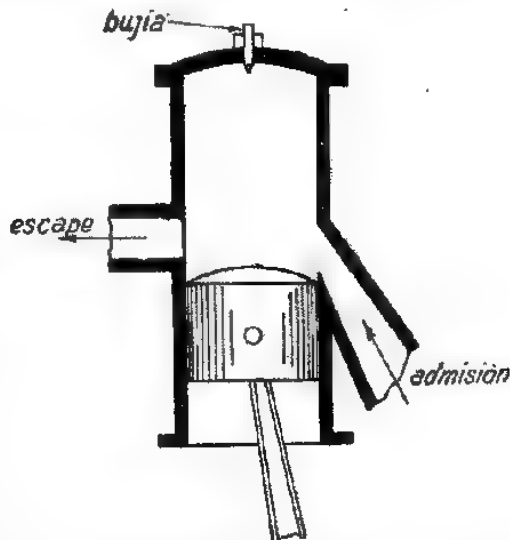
Corte esquemático de un motor a explosión de dos tiempos.
